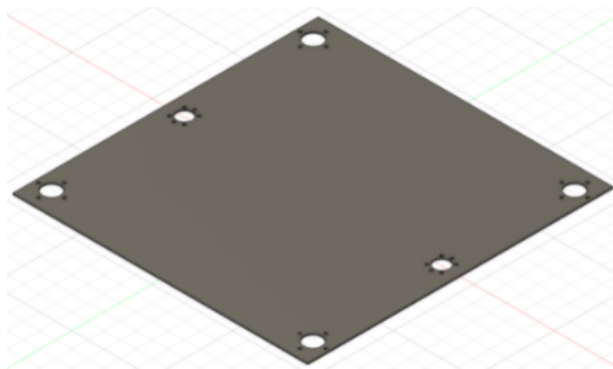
Especificações para corte e furação da placa ACM que será utilizada como suporte da bandeja, figura retirada do desenho técnico.
